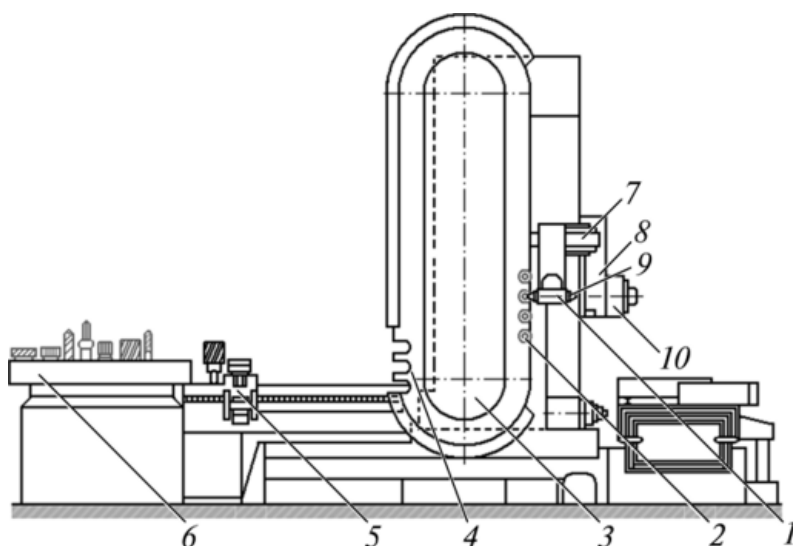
Схема устройства АСИ с перемещающимся между магазином и шпинделем автооператором:
